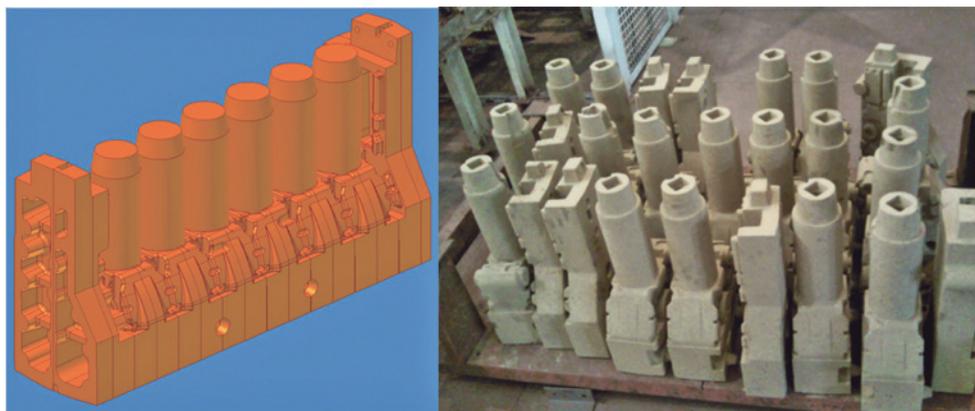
Стержневой пакет блока картера (фото слева), а также отдельные центровые и торцевые стержни (фото справа) для отливок 6-цилиндровых рядных блоков грузовых двигателей «Вейфанг»
